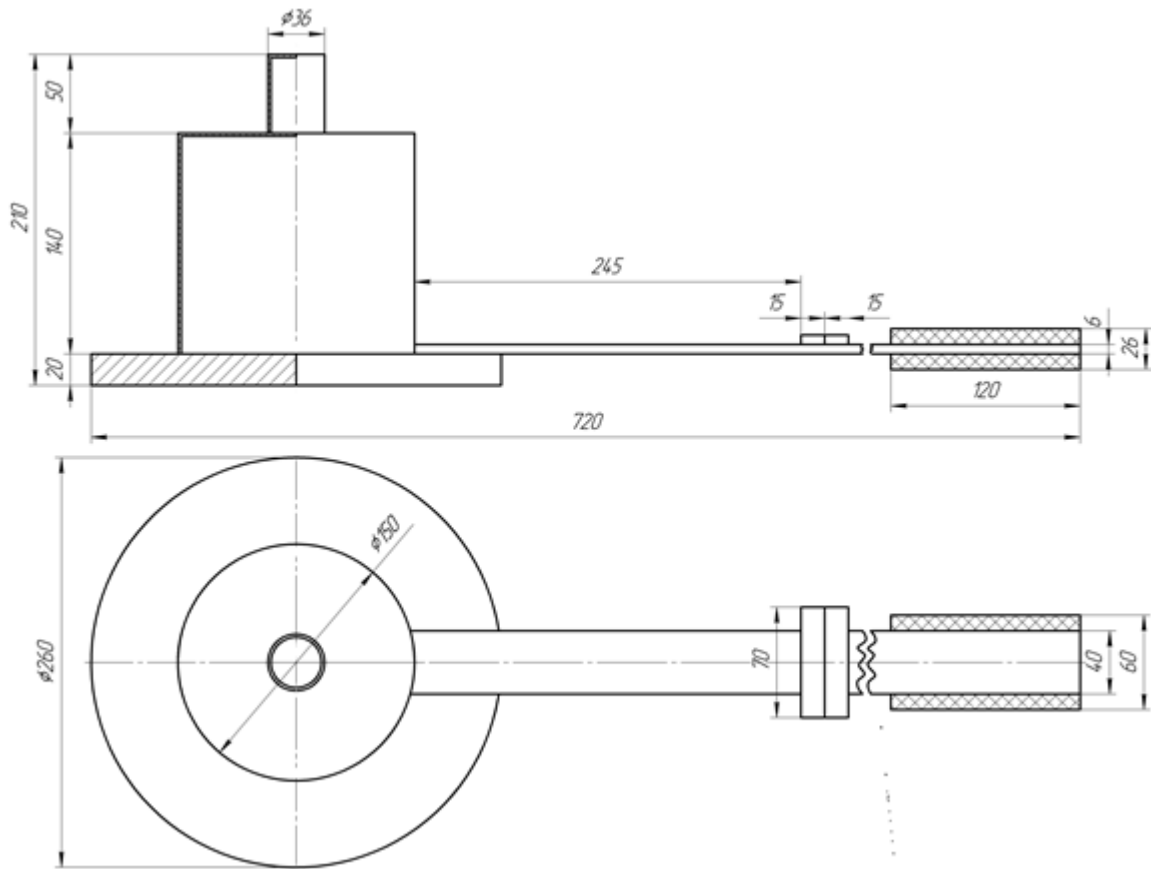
Пристрій для приварювання ремонтних вставок до остова дискового сошника зернової сівалки
